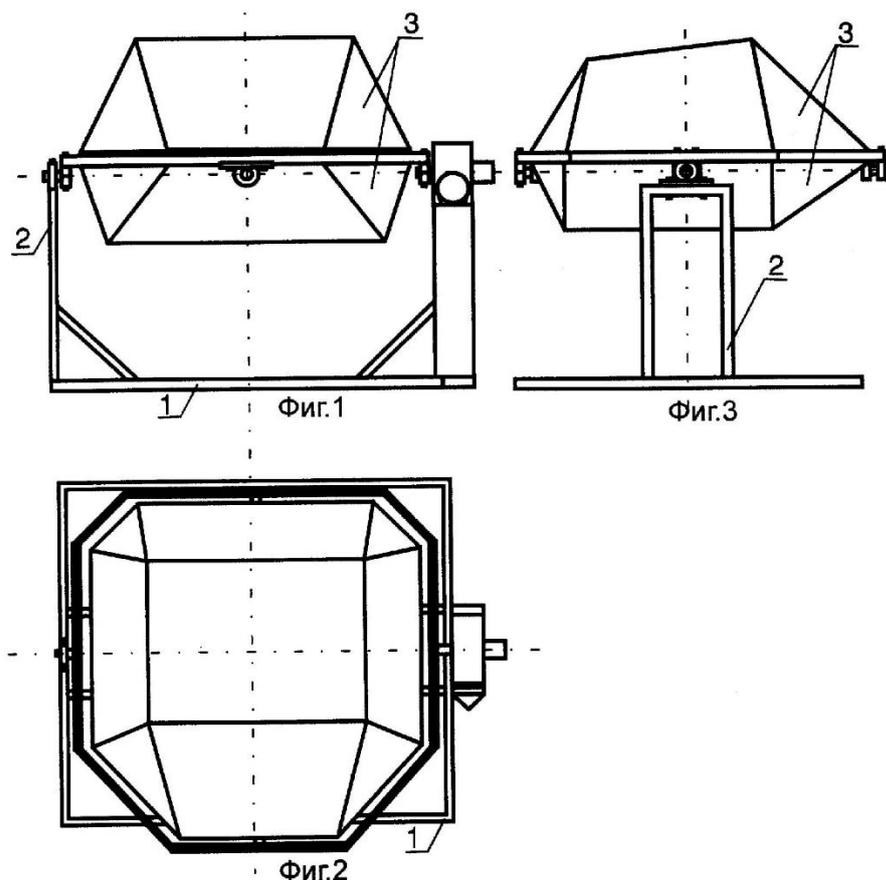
Общий вид конструкции [46]
